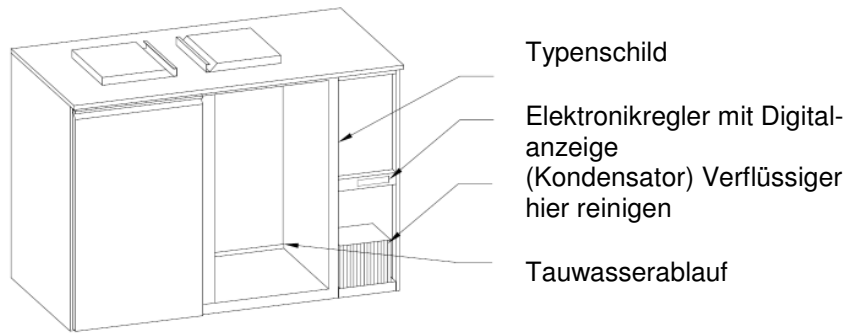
Draufsicht Abfallkühler, Eigenkühlung, steckerfertig
